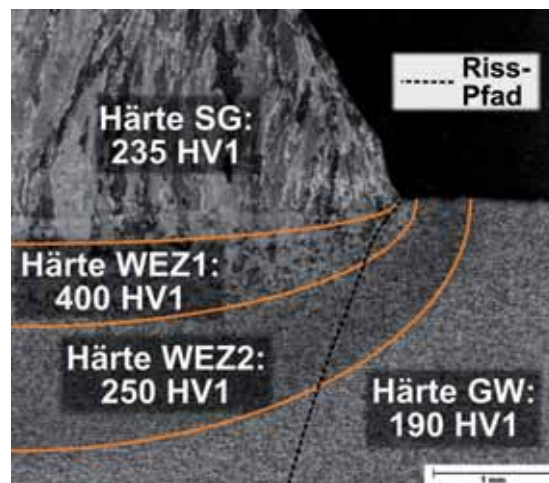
Mittlere Härte der einzelnen Gefügezonen (Schweißgefüge, Wärmeeinflusszone und Grundwerkstoff) in der Schweißnaht
